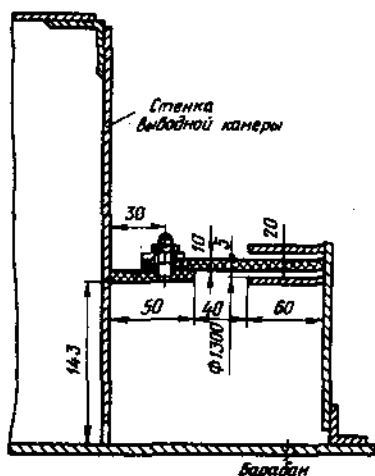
Конструкция уплотнения барабанной сушилки
